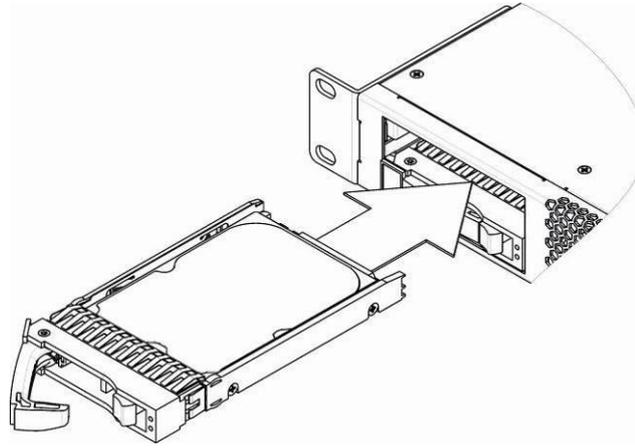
Монтаж SATA-диска в корпус устройства
